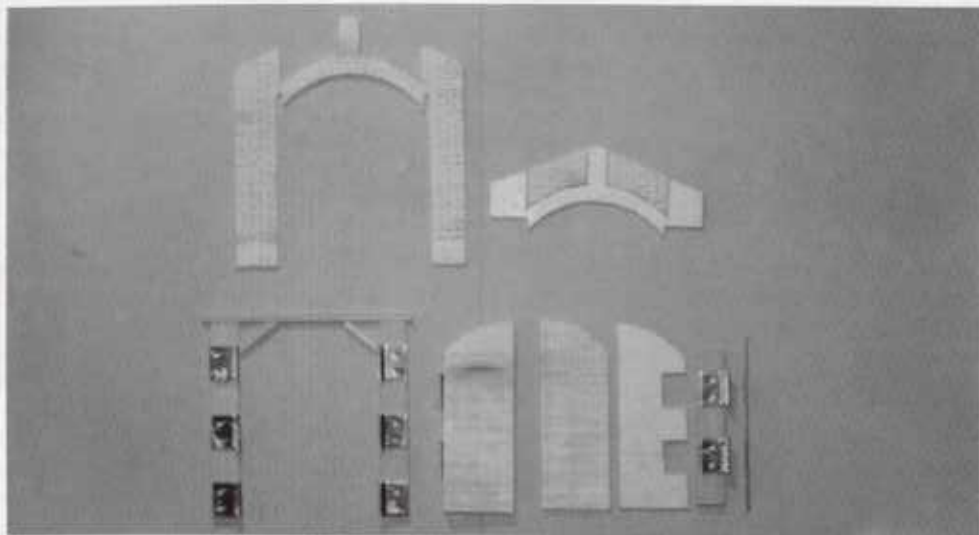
Aufbau der Seite mit dem Tor. Oben: Die eingerückte Mauer erfordert zwei Balsaholzplatten, die hintereinander geklebt werden. Unten links: Grundgerüst mit "halben" Scharnieren. Unten rechts: Aufbau des Tores: Bretterwand aus Balsaholz, Karton, Holzprofil mit Scharnier, Scharnierstift (Draht).
